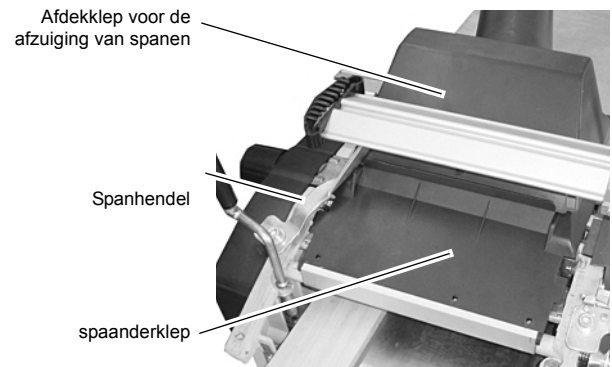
Afdekklem voor de afzuiging van houtspanen op spaanderklep
